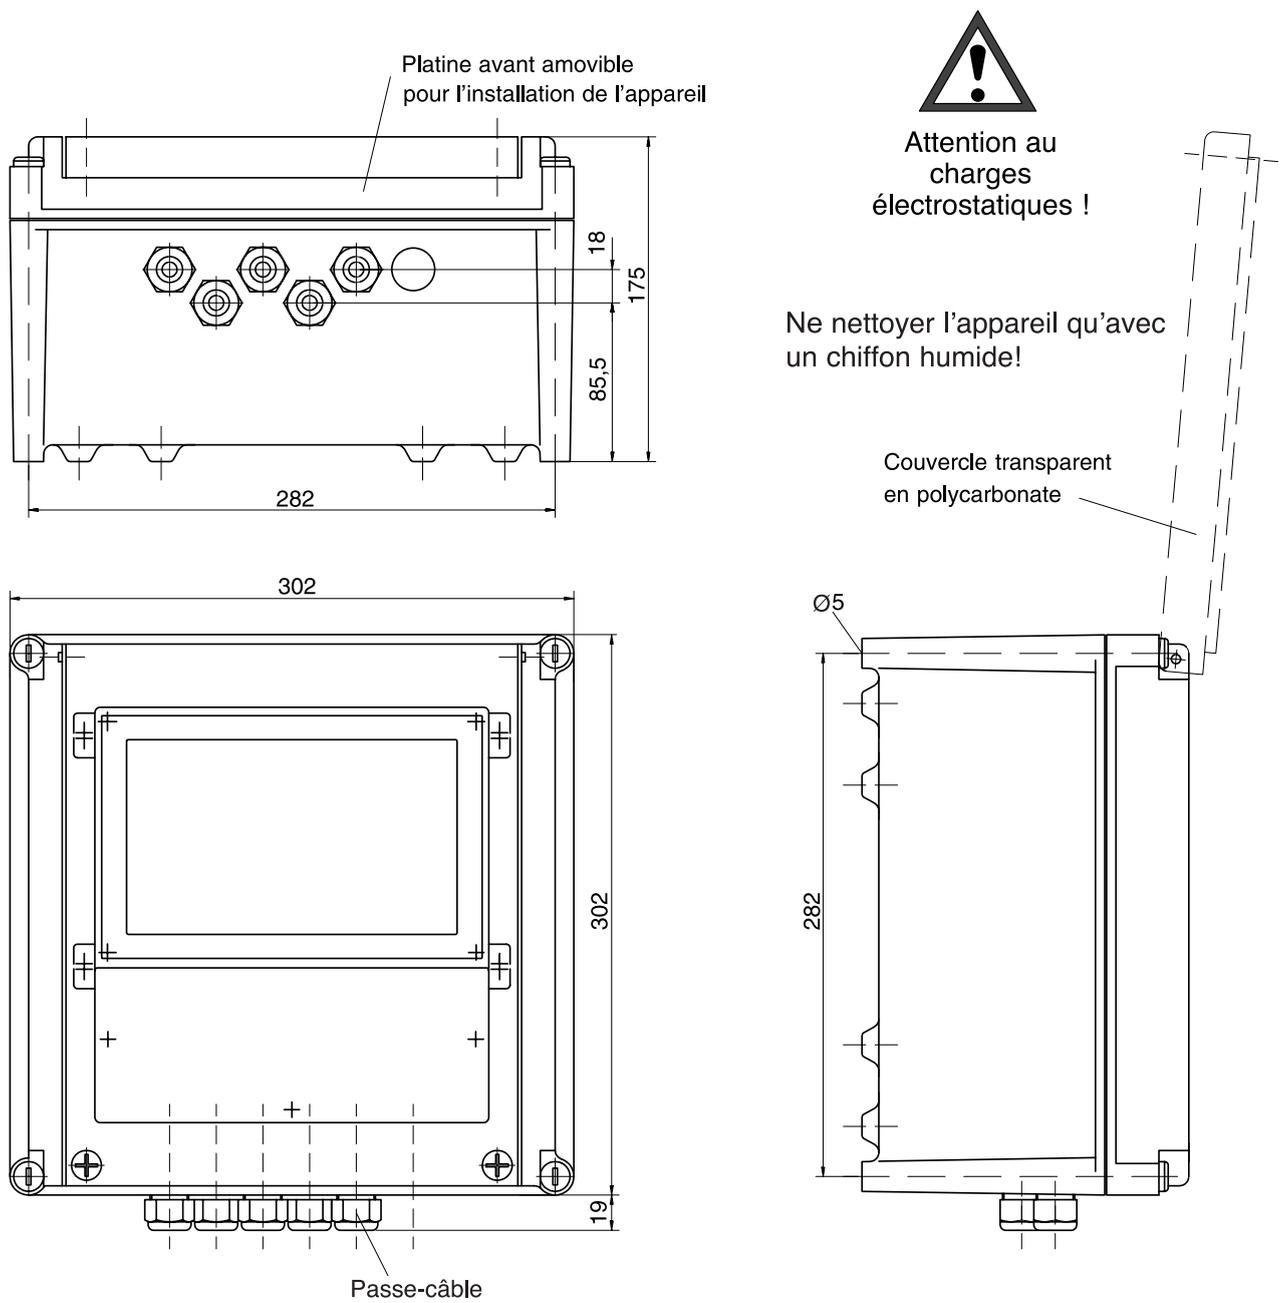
Dessin coté boîtier de protection ZU 0158
